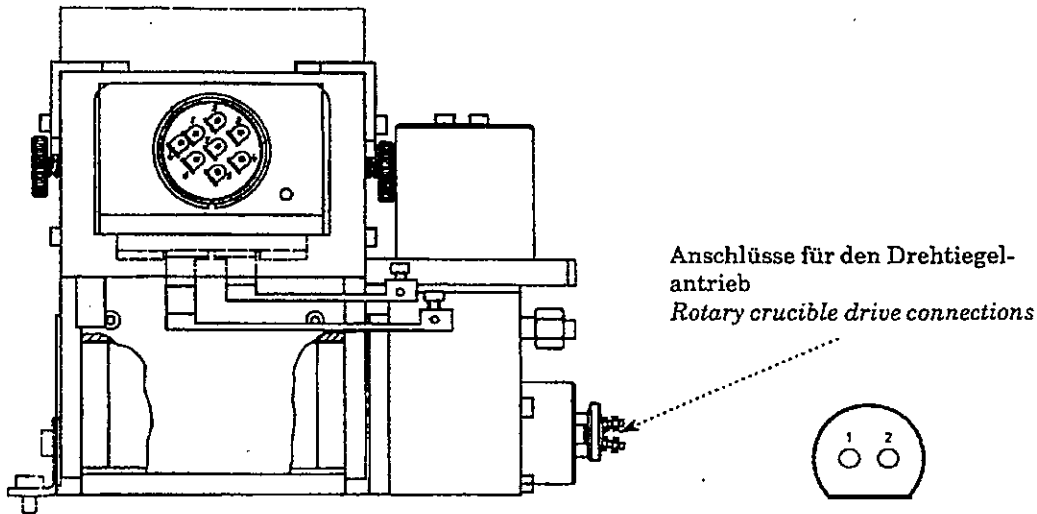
Anschlüsse des Drehtiegelantriebes
